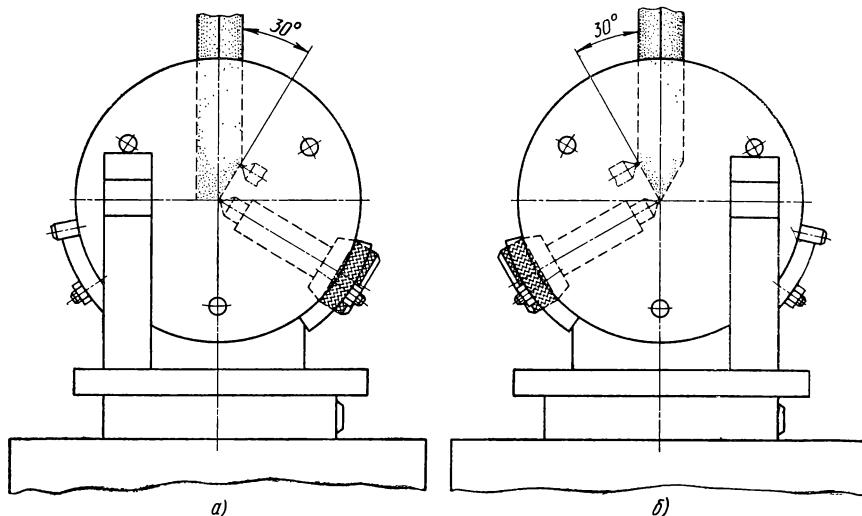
Схема настройки универсального приспособления для профилирования круга:
